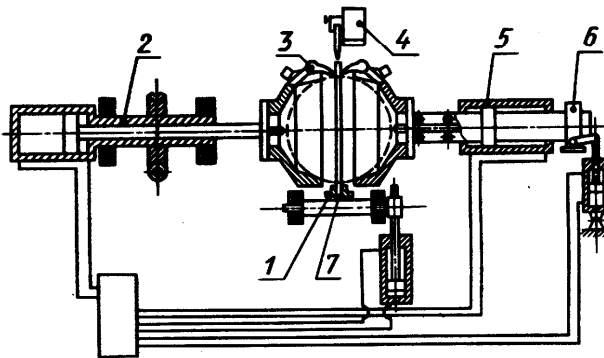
Схема станка-автомата для сборки и сварки пустотелых шаров из двух полушар
